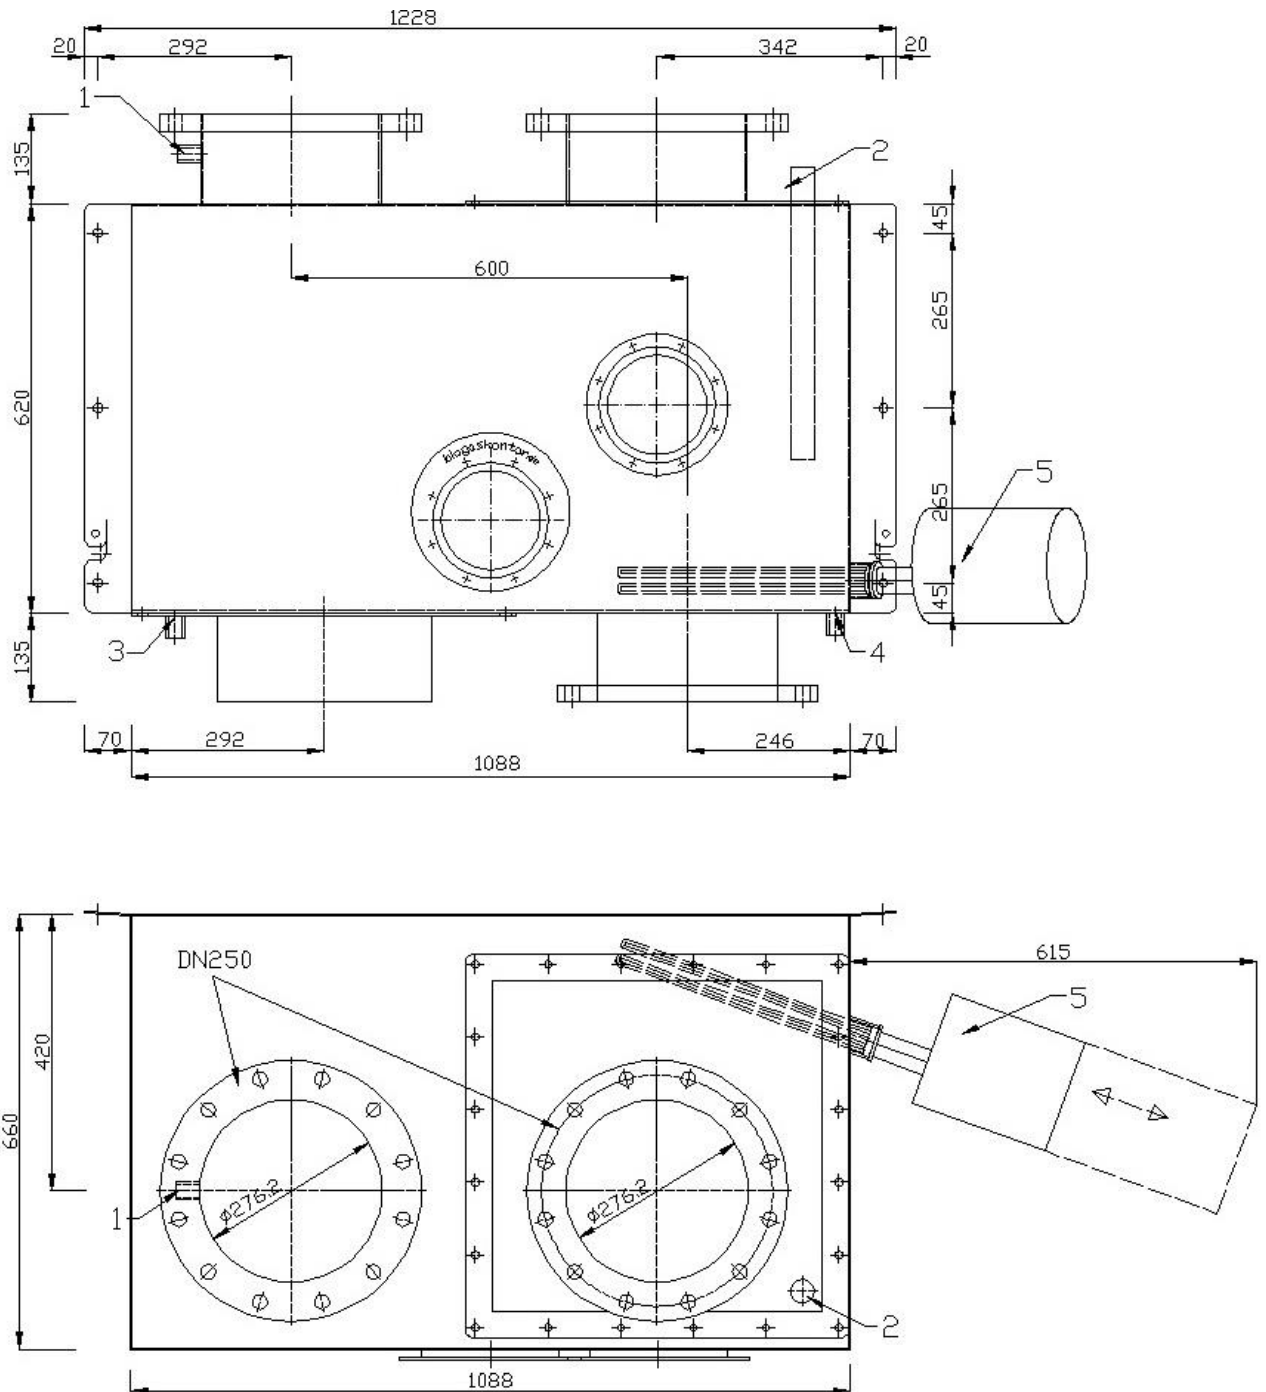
dimensions du régulateur de pression ÜU-TT 273
